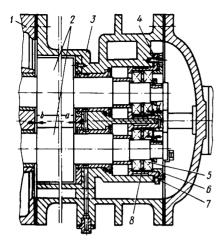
Винтовой компрессор 5BX-350/2,6 (сборка):
